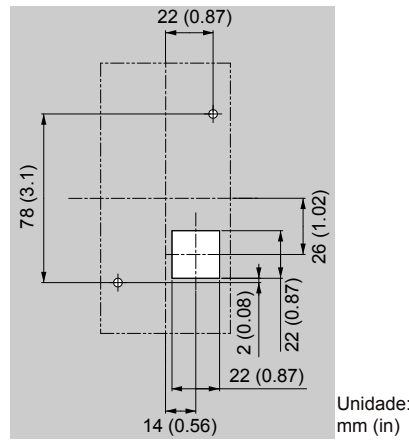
Dimensões de corte do painel (instalação de montagem externa/na superfície)
